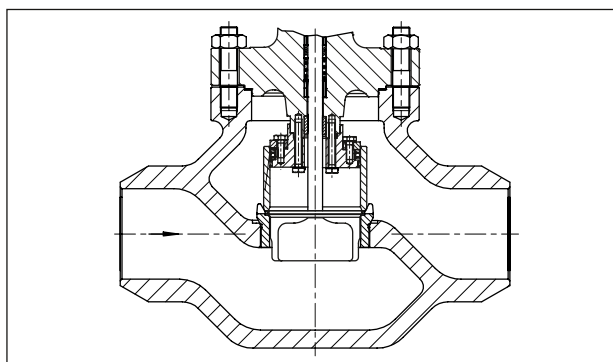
Ventil Typ 3251/3251-AM mit Anschweißenden und druckentlastetem Ventilkegel
